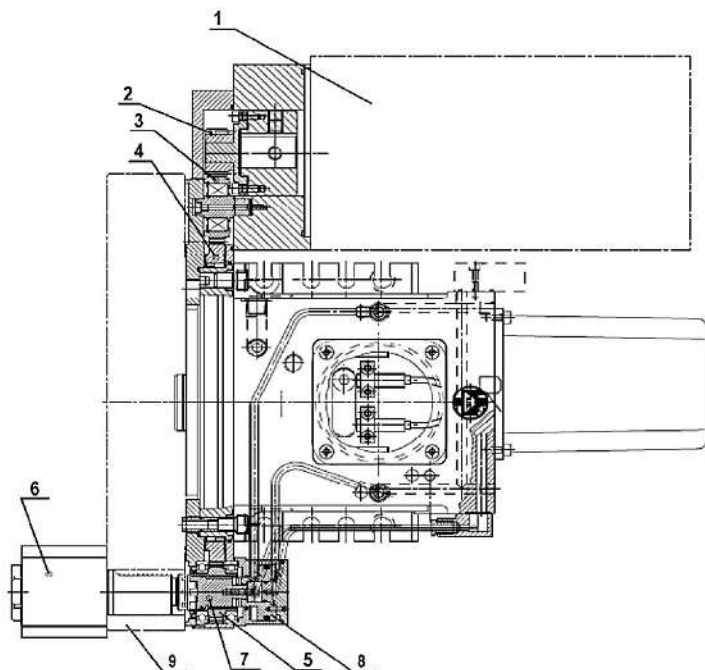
Револьверна головка Varuffaldi TBMA
